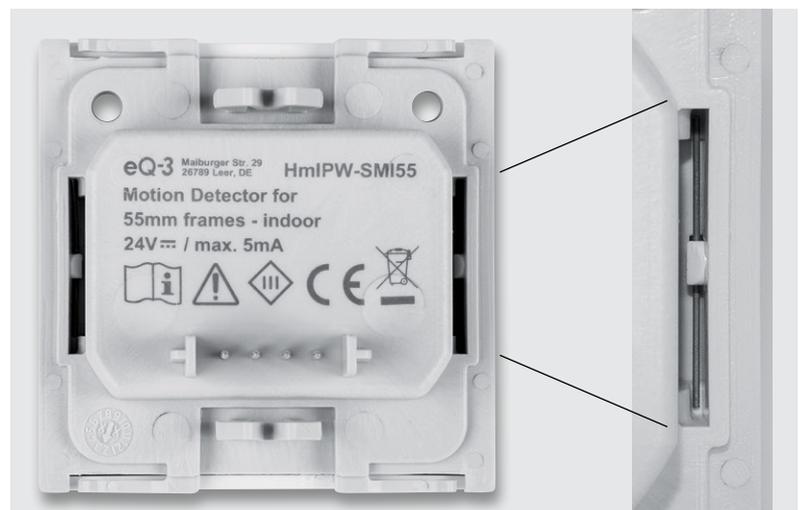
So sind die Federdrähte für die Tasterwippe einzusetzen.
